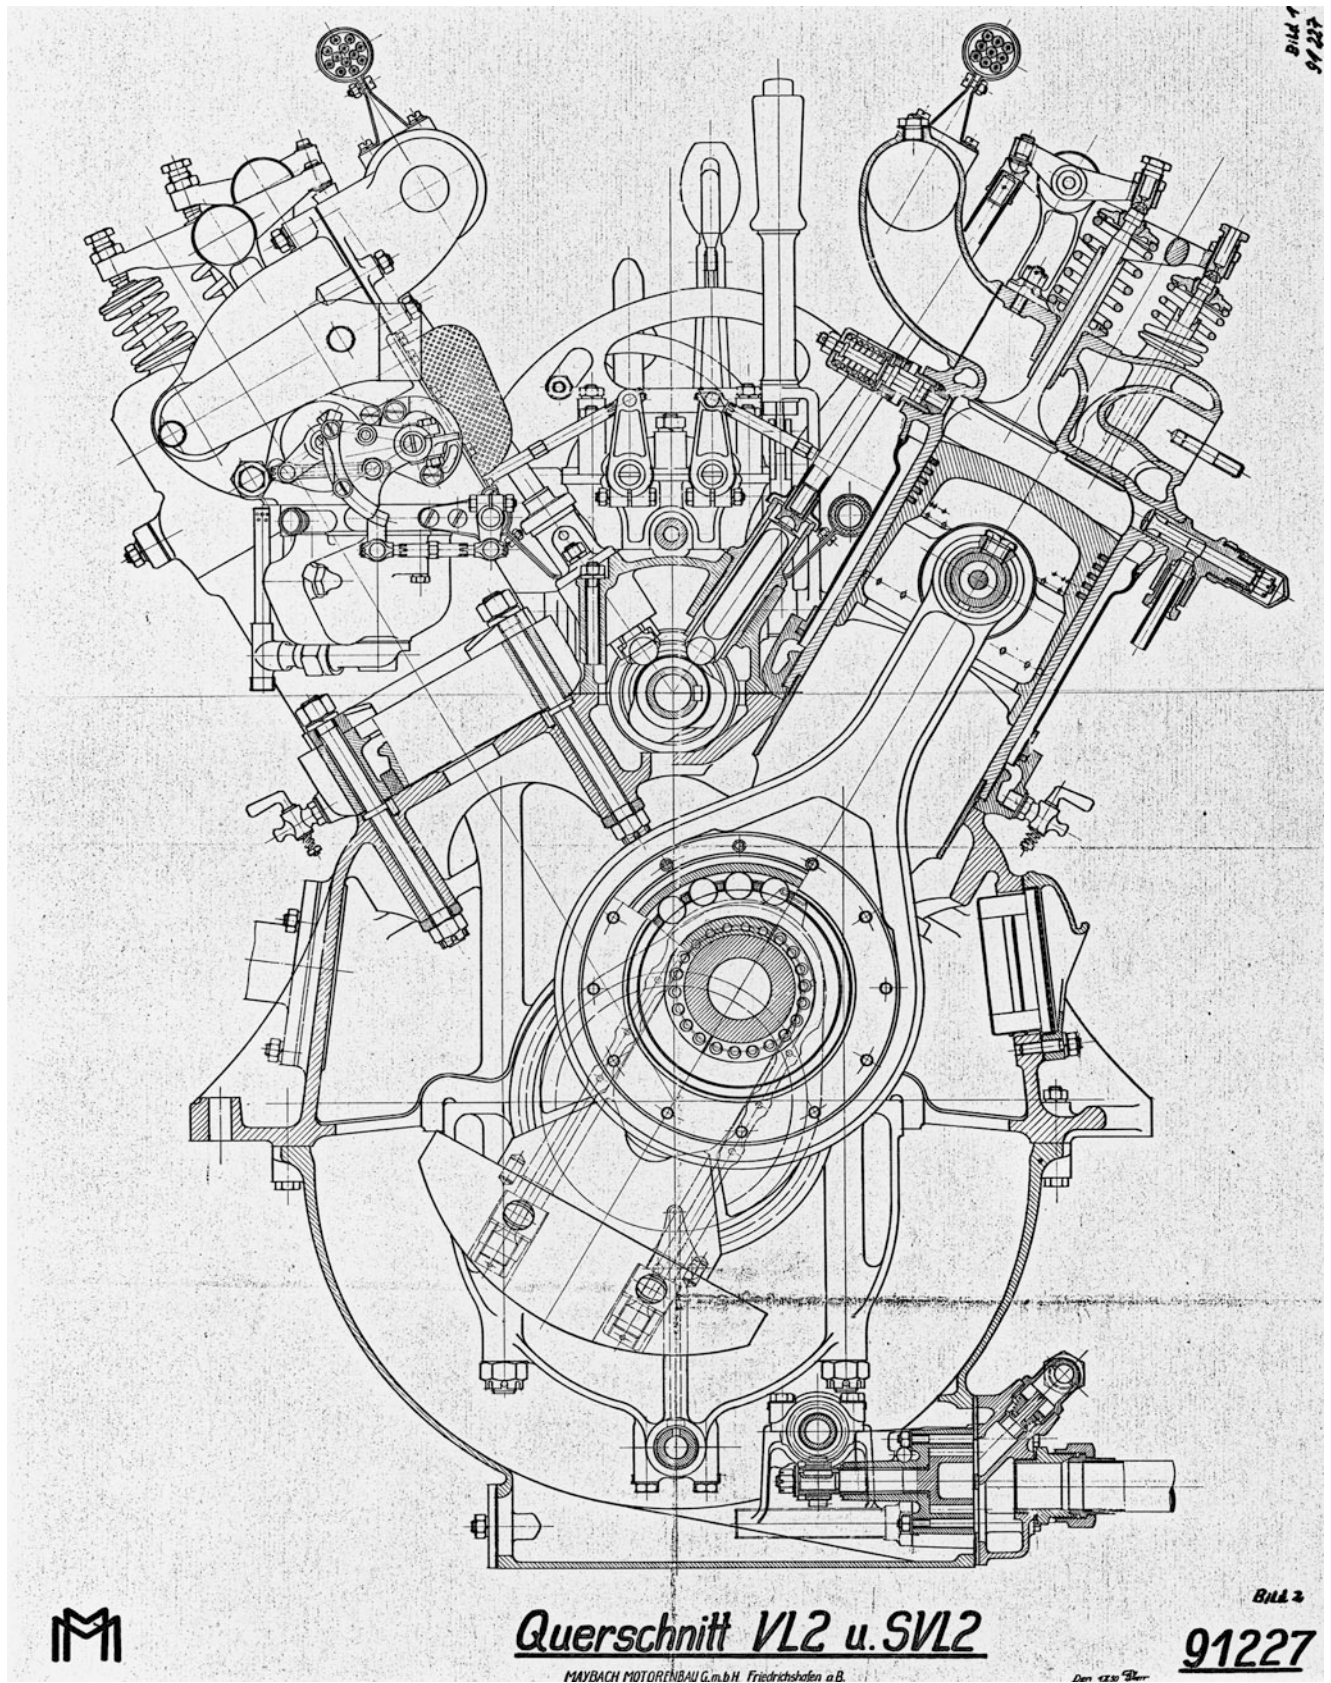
Querschnitt des Luftschiffmotors VL 2 (Schiffsausführung: SVL 2): wassergekühlter Viertakt-Ottomotor in Zwölfzylinder-V-Bauart, umsteuerbar, rollengelagertes Triebwerk; Bohrung 140 mm, Hub 180 mm, Hubraum 33.234 cm³, Leistung 419 kW (570 PS) bei 1.600 min⁻¹
